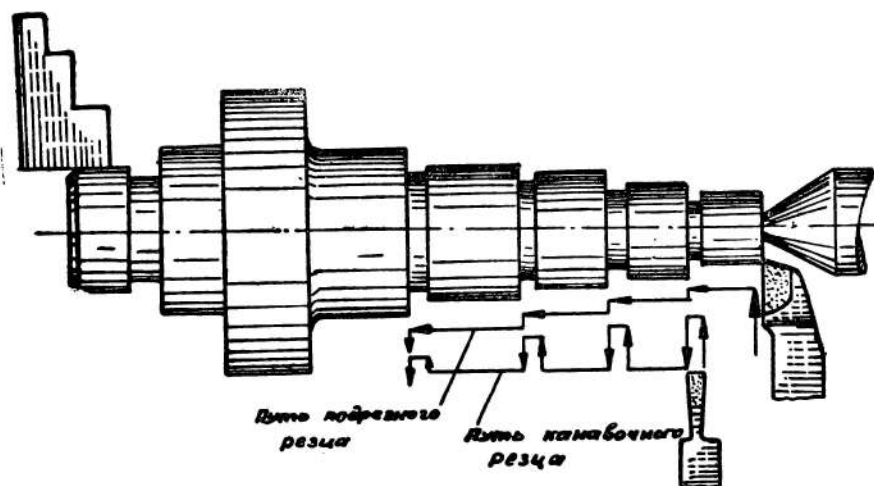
а. Новый способ обработки ступенчатых валов по способу токарей Лакура и Воробьева
